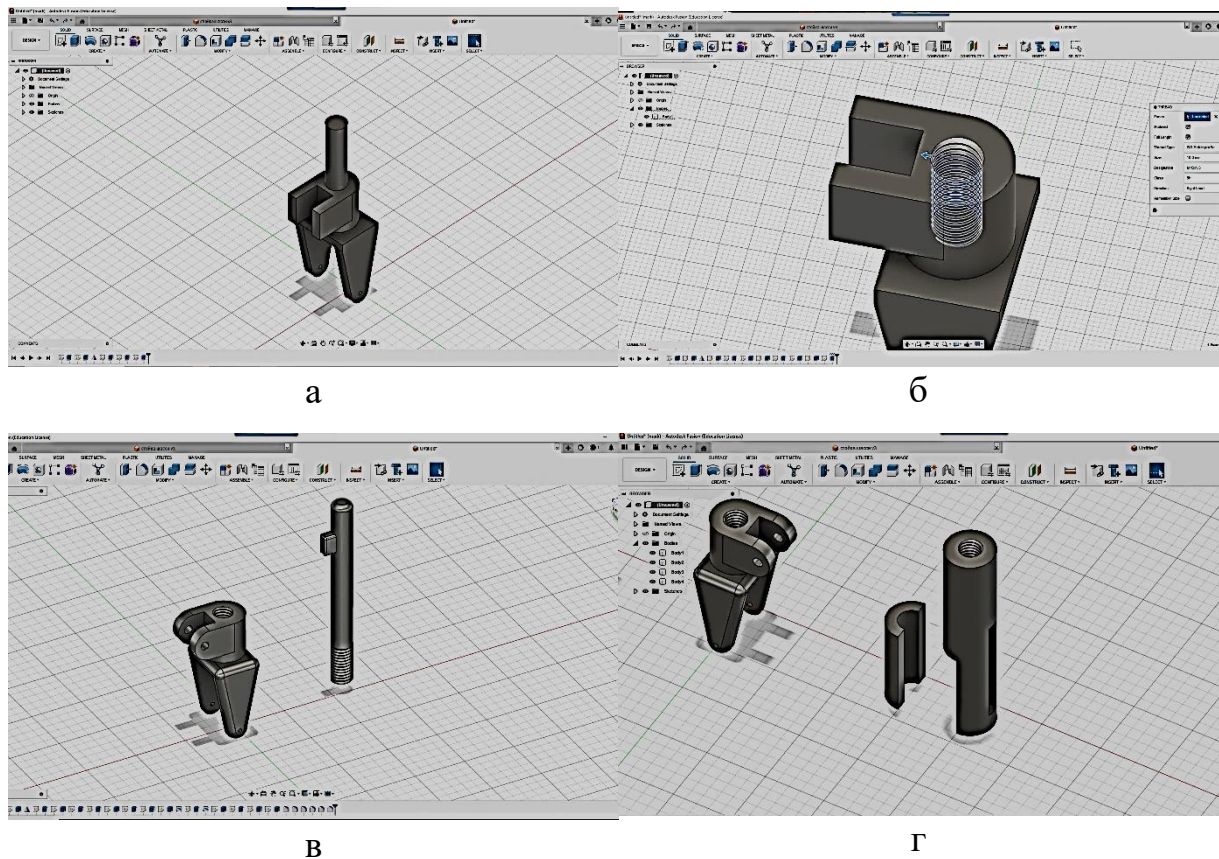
Етапи створення моделі в середовищі Fusion 360; а) основна заготовка; б) створення нарізі командою THREAD; в) закруглення кутів за допомогою команди FILLET; г) вигляд трьох деталей
